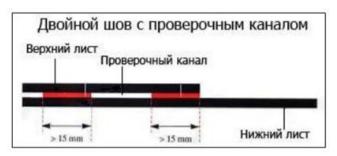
Схема сварочного стыка/нахлеста.
